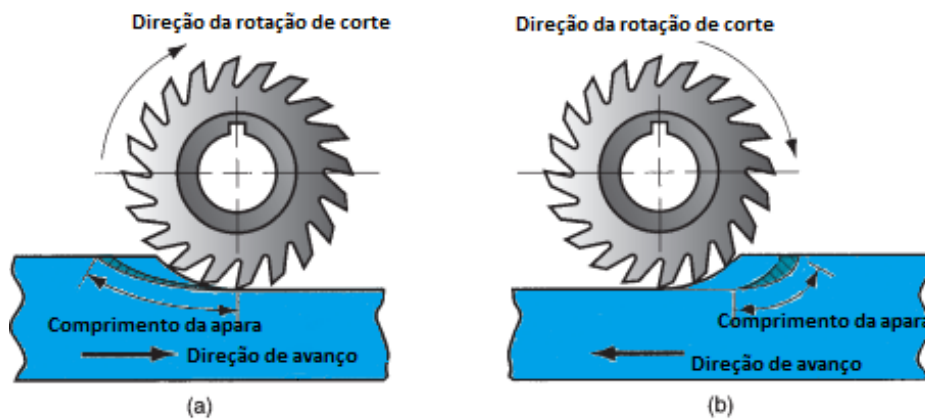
Tipos de fresagem cilíndrica: (a) empurrar e (b) puxar [27].
